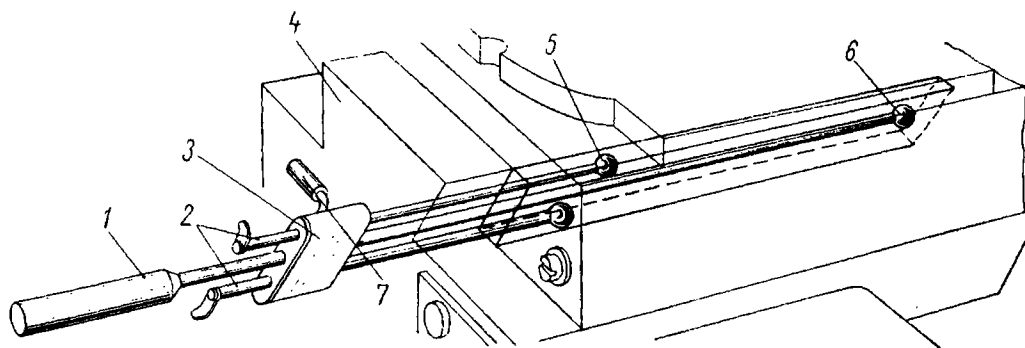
Щуп для измерения щелевых отверстий для клиньев
